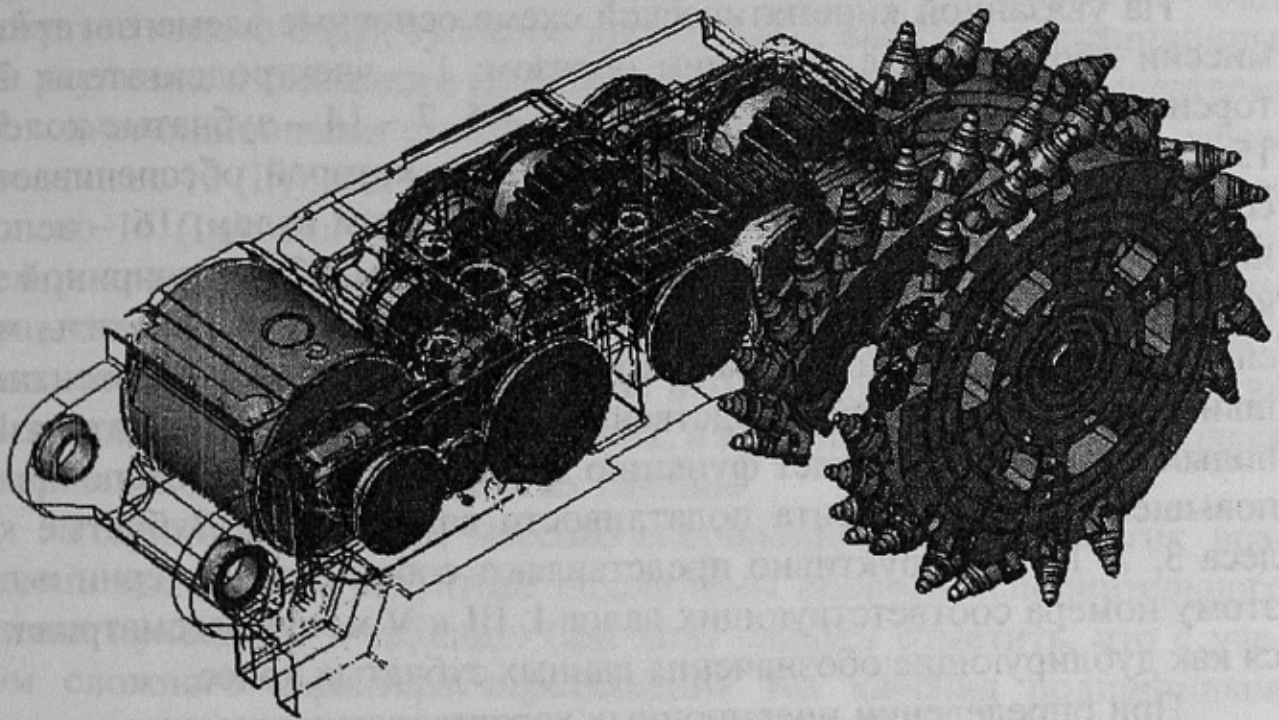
Трехмерная модель поворотного блока резания комбайна КДК500 I типоразмера
